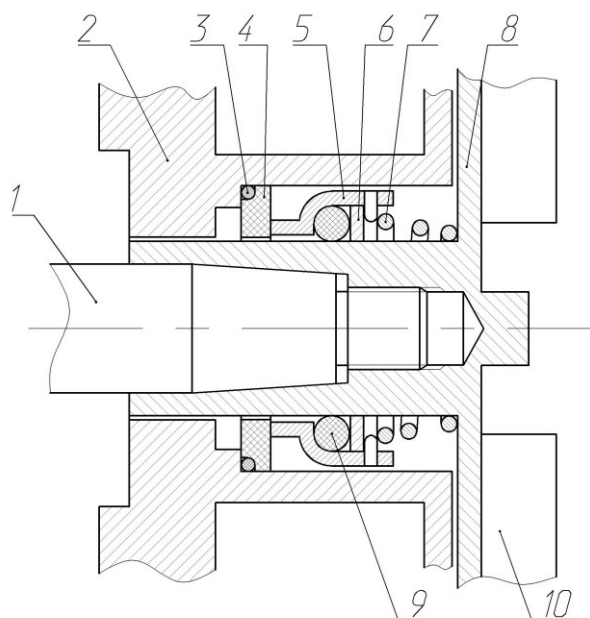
Торцевое уплотнение вала рабочего колеса: 1 – вал рабочего колеса; 2 – корпус; 3 – кольцо уплотнительное; 4 – неподвижное кольцо уплотнения; 5 – подвижное кольцо уплотнения; 6 – шайба; 7 – пружина поджимная; 8 – рабочее колесо; 9 – кольцо уплотнительное; 10 – лопасть рабочего колеса.
